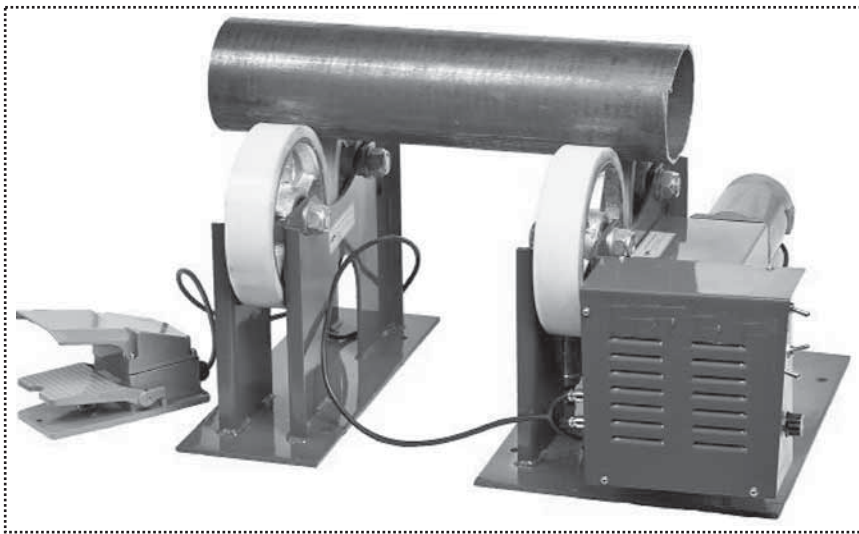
Сварочный вращатель NHTR-6000
